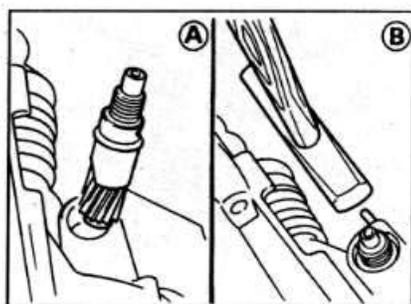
А.16. Установка ведущей шестерни привода спидометра (А) и фиксация ее цилиндрическим штифтом (В).
